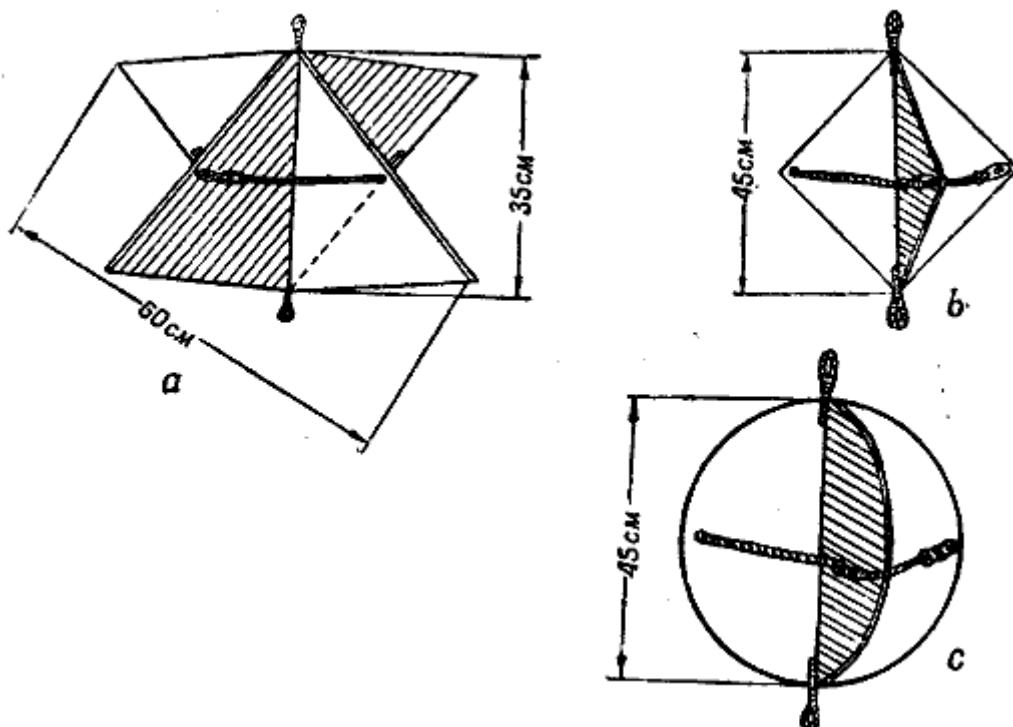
Складывающиеся радиолокационные отражатели из легкого металла: a — ромбовидной формы, b — квадратной формы; c — круглый, для одновременного использования в качестве якорного шара
